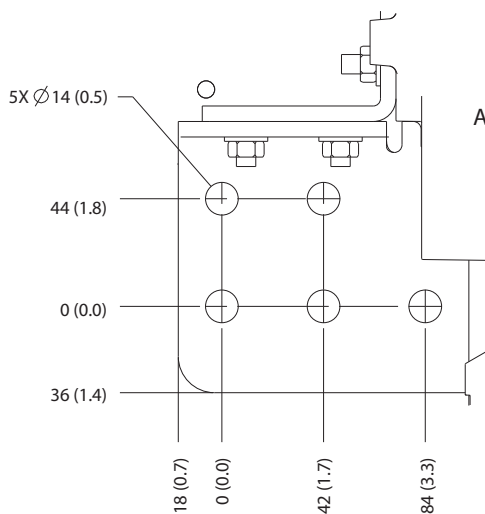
Dimensions des bornes de secteur, moteur et terre E3h (vues latérales)
